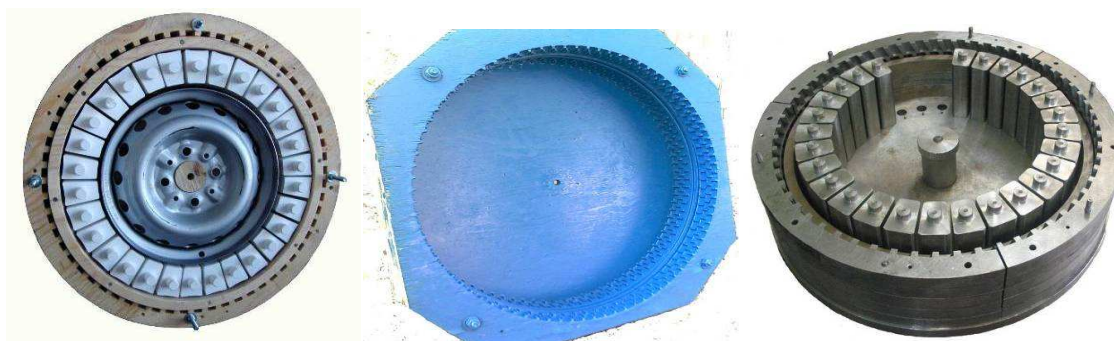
Матрицы для изготовления колес с безвоздушными шинами
